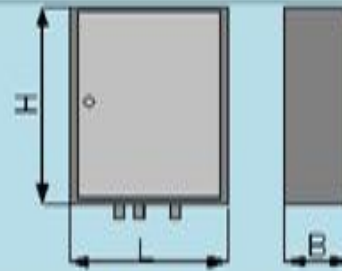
Общий вид и габаритные размеры РУСМ8000
